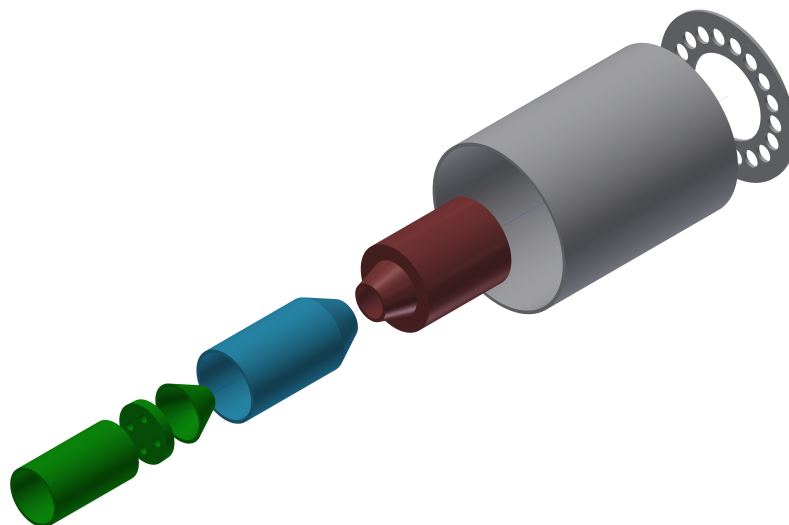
Vista en explosión del inyector de la turbina a gas
